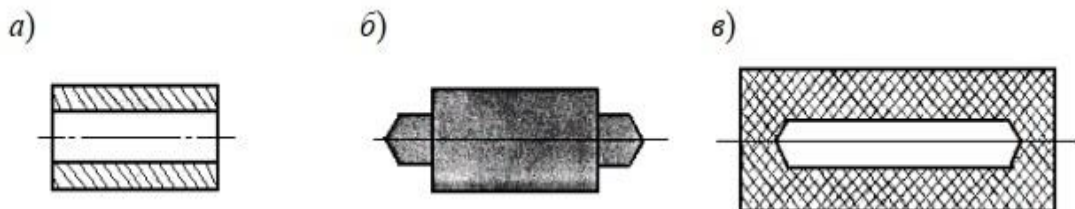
Креслення деталі втулки (а), моделі виливки (б), стрижневого ящика (в)
